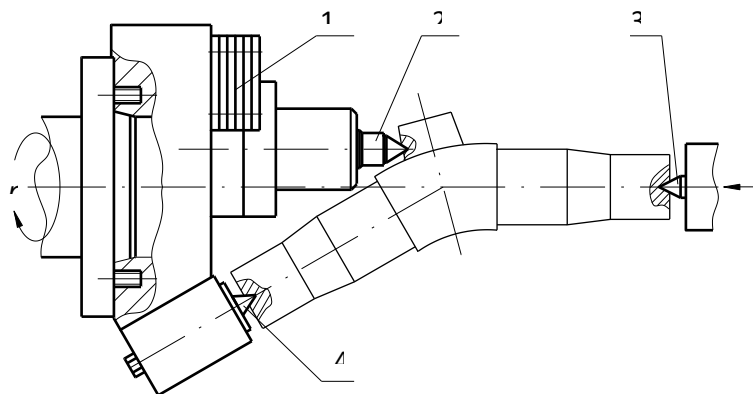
Базування й затиск криволінійної осі у пристрої токарного верстата (спосіб базування рис. 2а)
